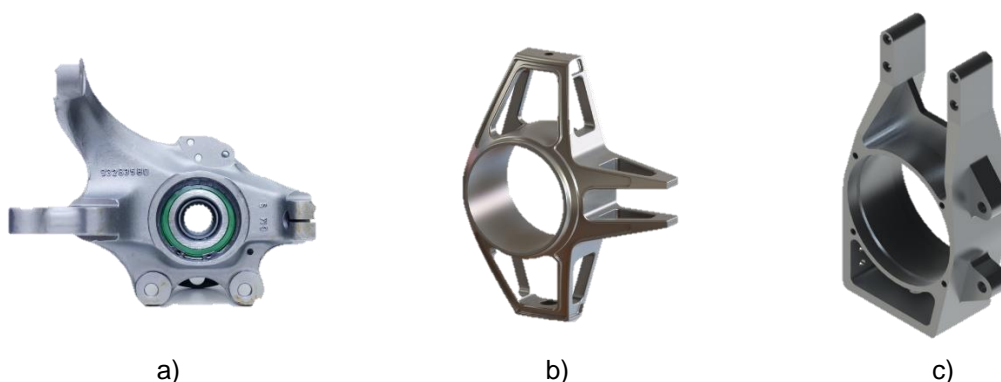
Exemplos de mangas de eixo: a) ferro fundido/ aço forjado; b) alumínio fundido c) Usinagem CNC a partir de bloco de alumínio.
